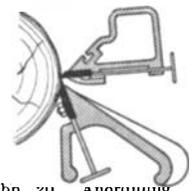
Anordnung der Schnittwerkzeuge einer Schälmaschine (Fleck).
